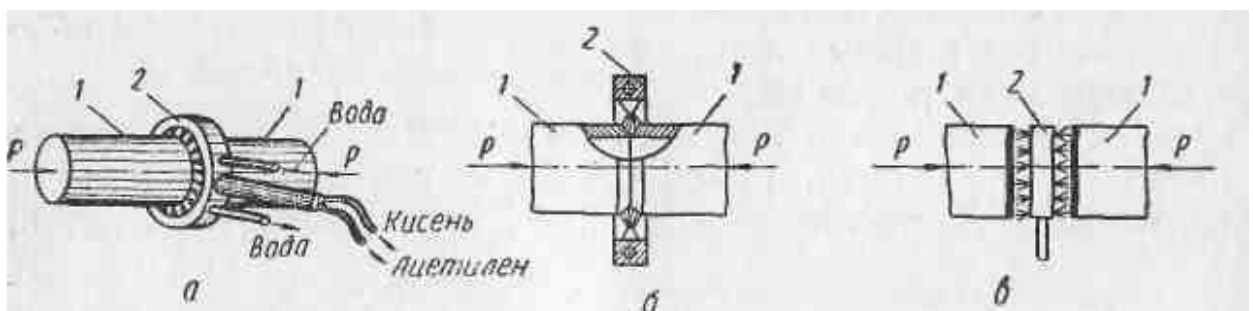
Схеми основних видів газопресового зварювання:
